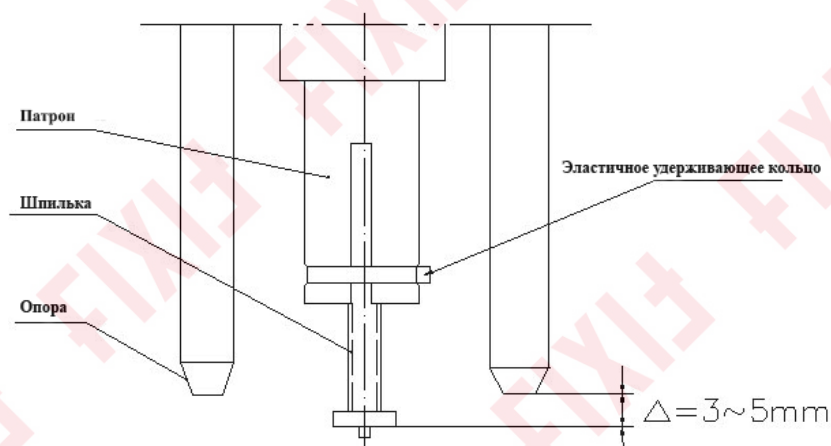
Регулировка выступа сварочного пистолета
